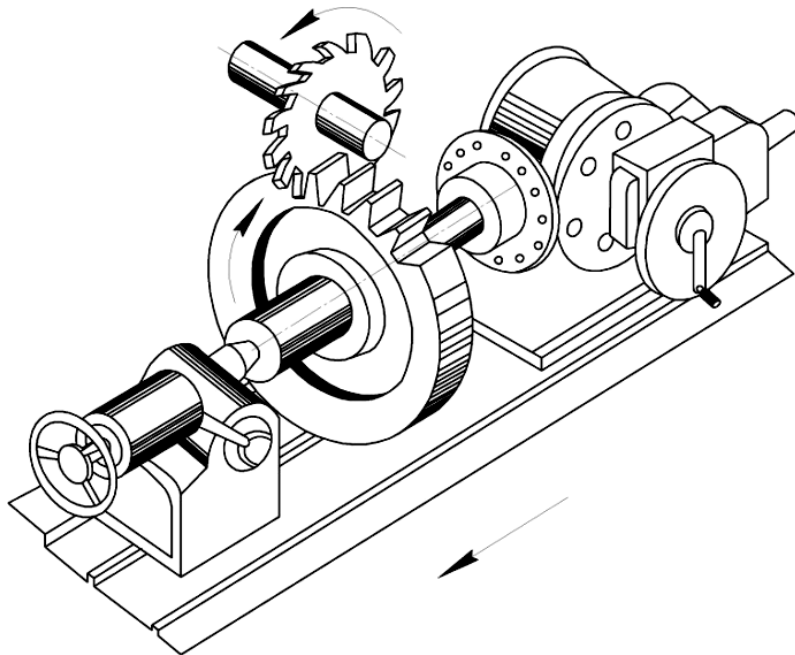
Схема нарізування зубів за допомогою ділильної головки
